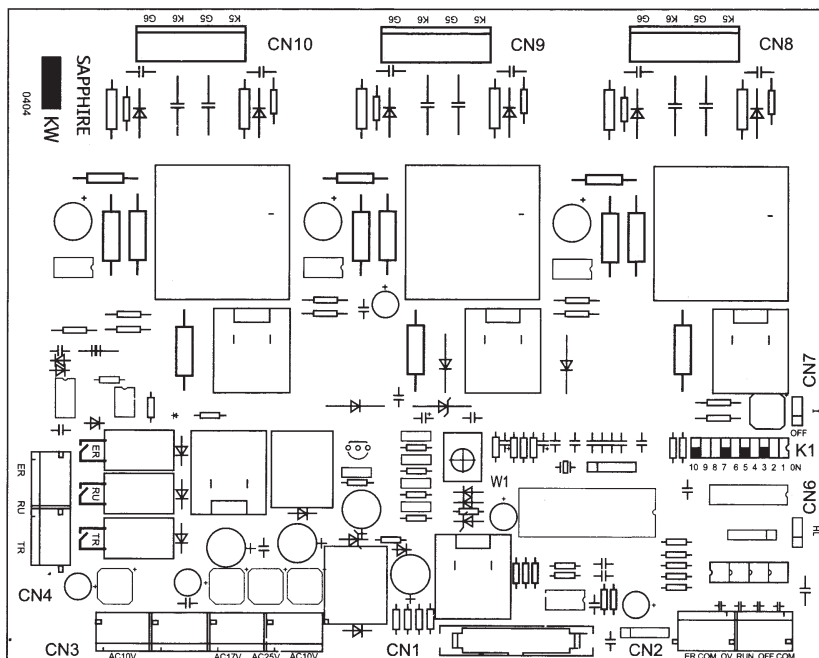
SAP300 软起动器 PCB 板元器件布置图
